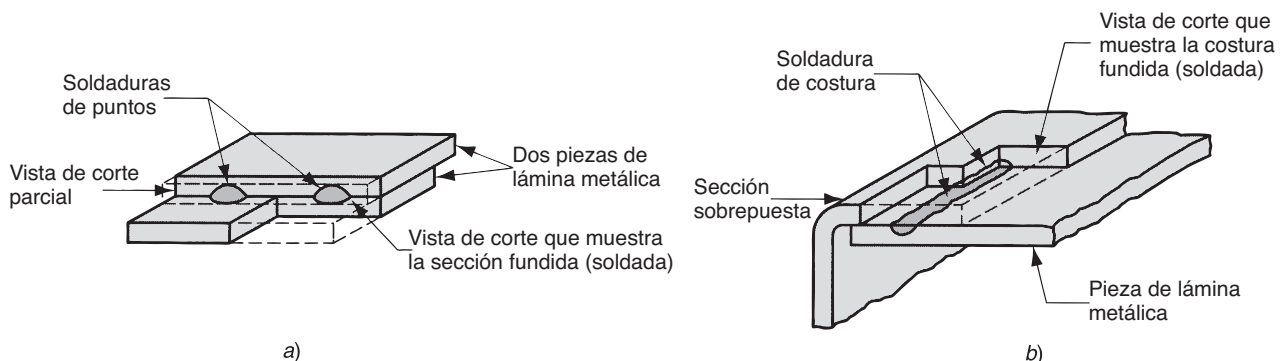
a) Soldadura de puntos y b) soldadura de costura.
